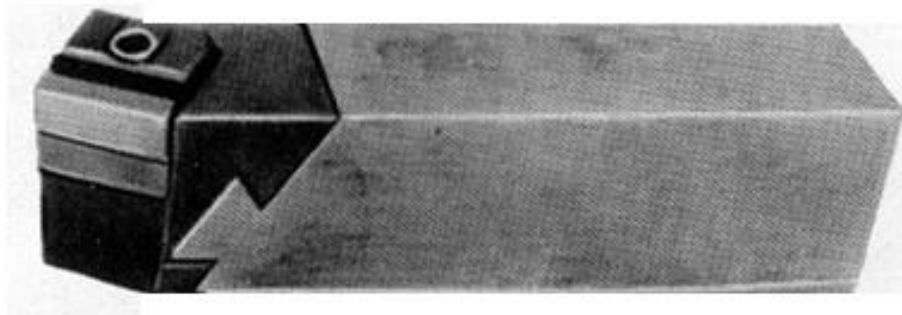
Збірний різець для чорнової обробки на важких верстатах токарної групи
